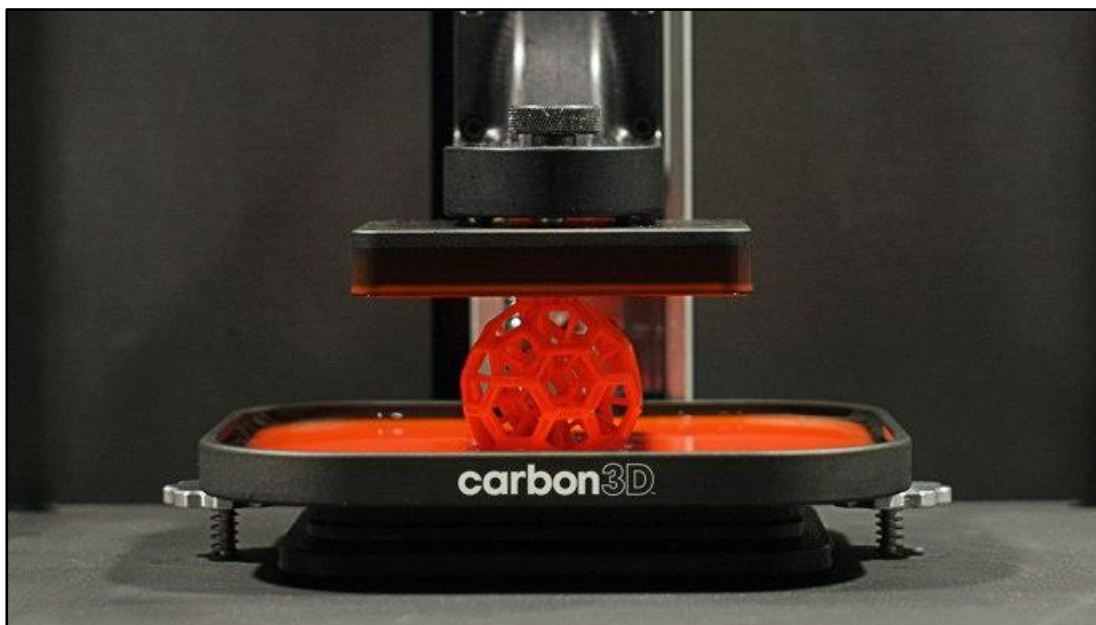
Impresión tridimensional mediante DLP de un elemento.
